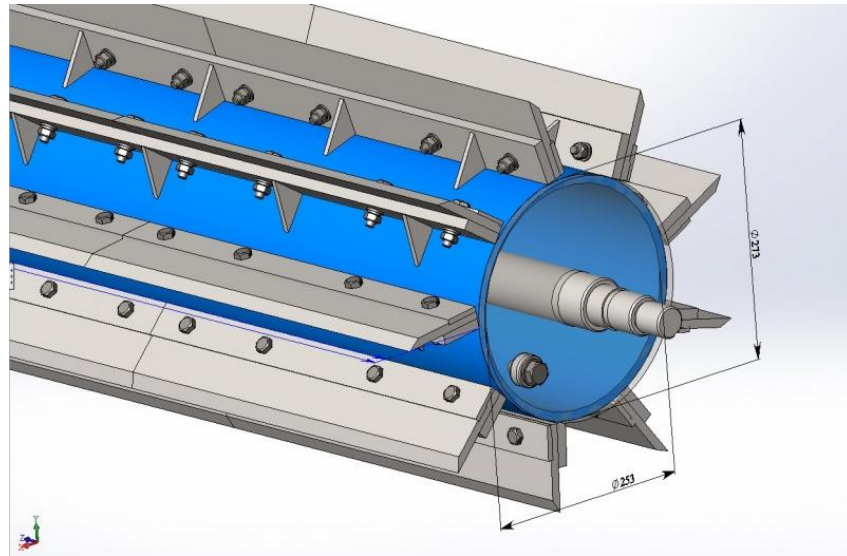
Конструктивна схема типового катка-подрібнювача барабанного типу
